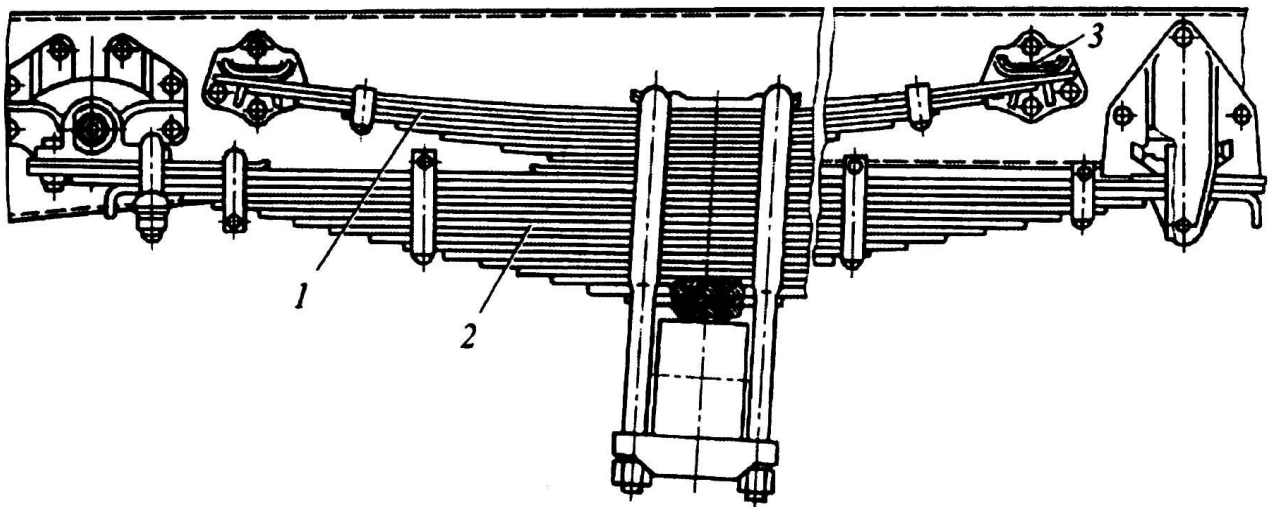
Ресорна підвіска з додатковою ресорою:
